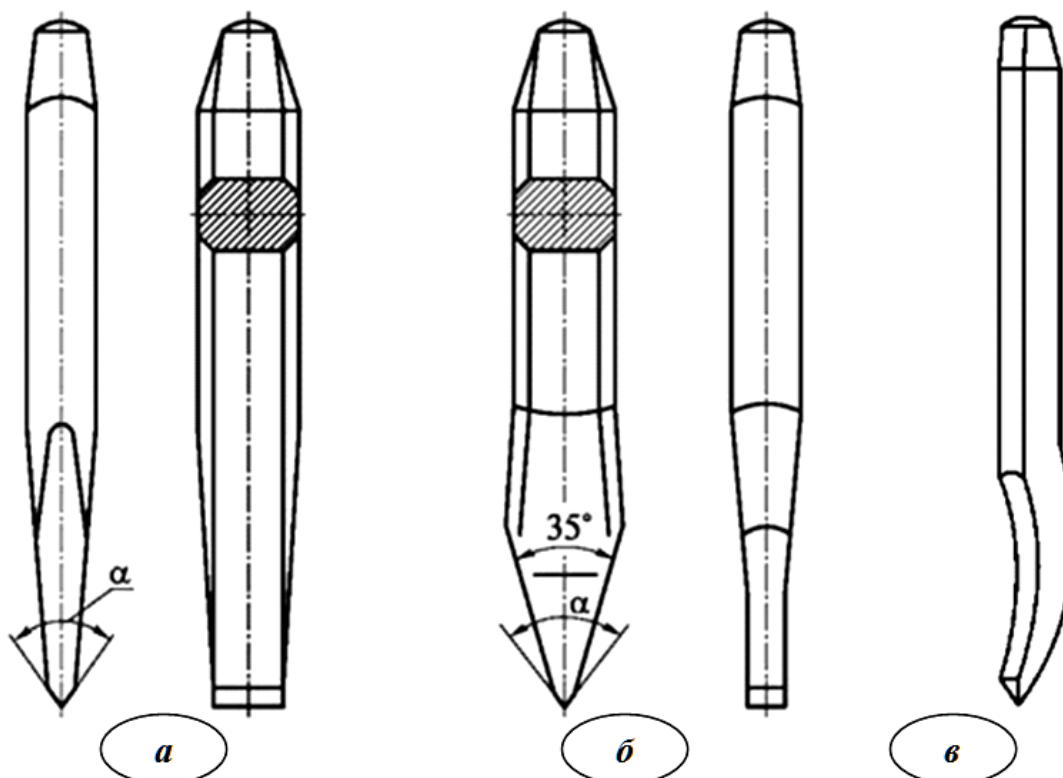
Інструменти для вирубування: а — зубило; б — крейцмейсель; в — канавочник; α — кут загострення інструменту
